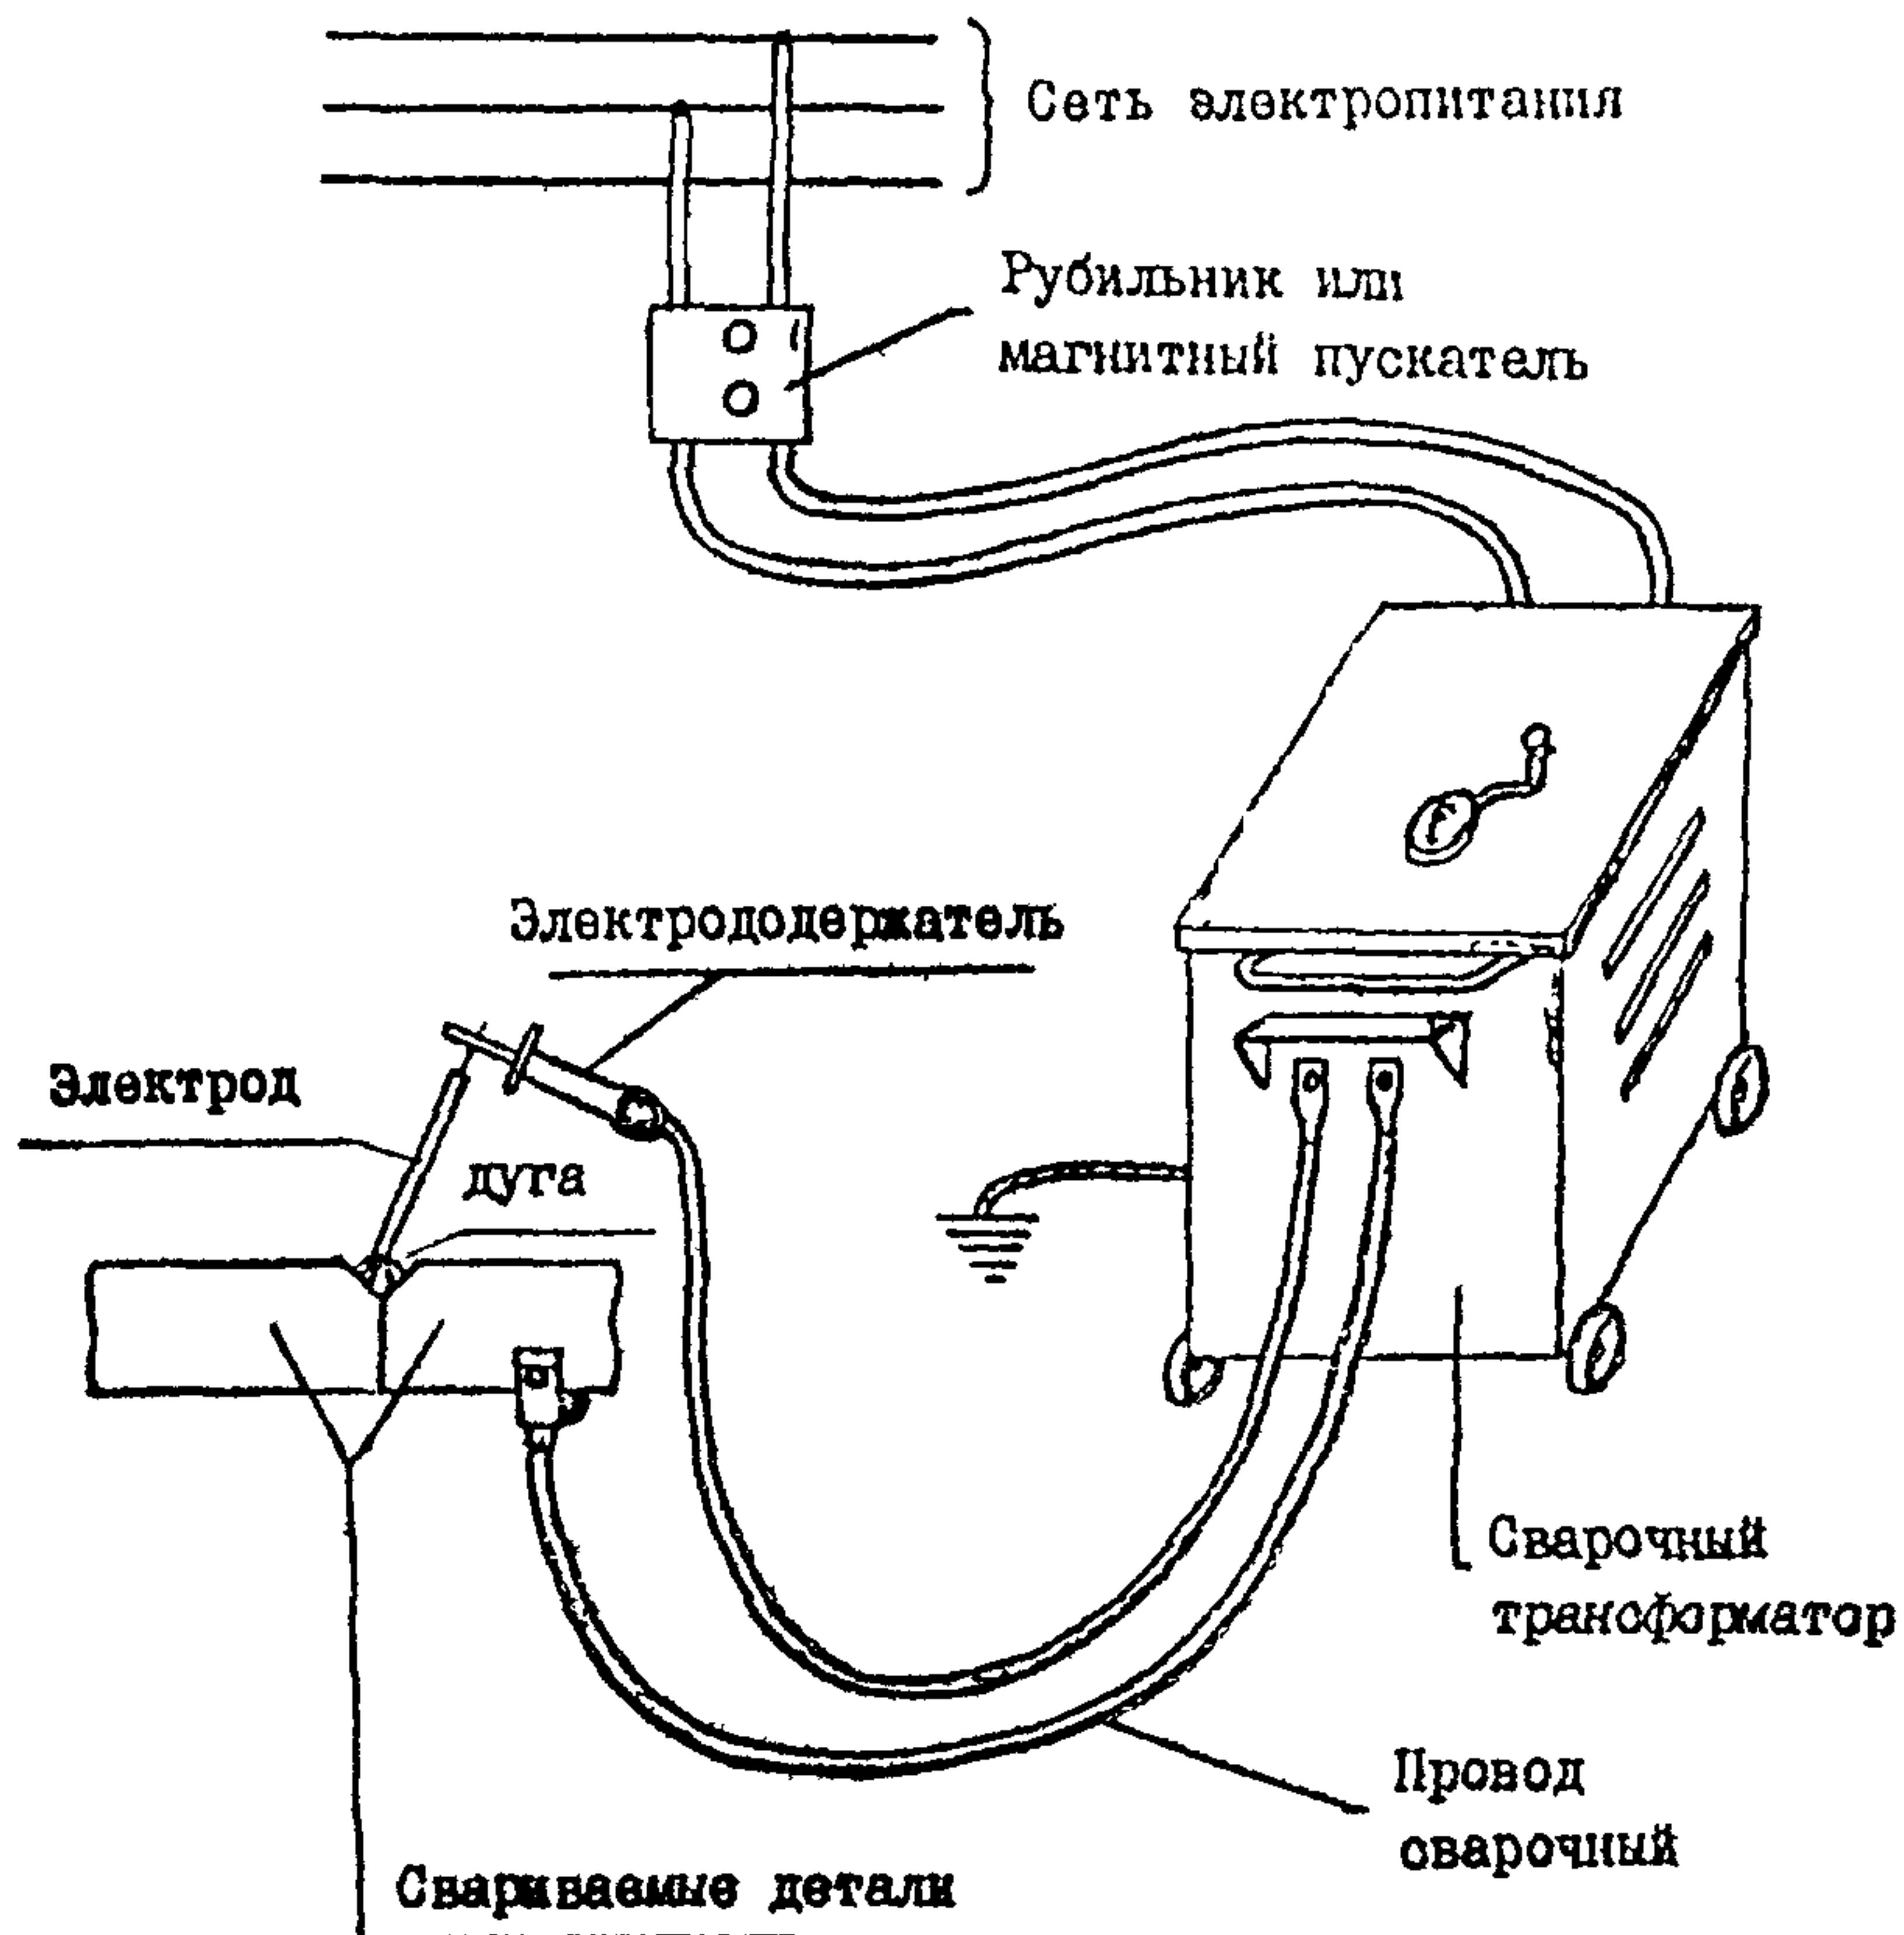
Схема соединения сварочного поста для ручной сварки
